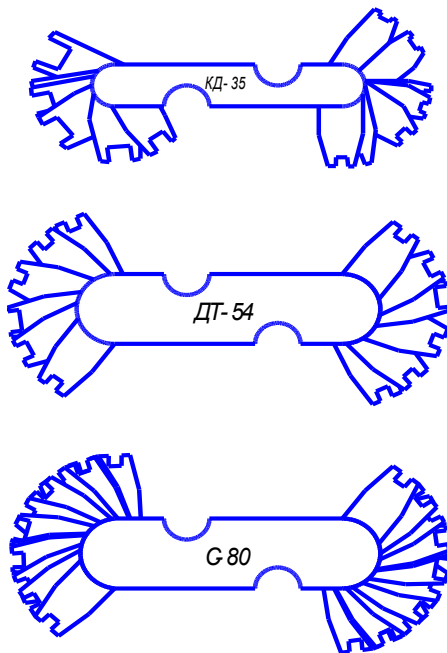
Предельные шаблоны для дефектовки шестерни по толщине зубьев.
